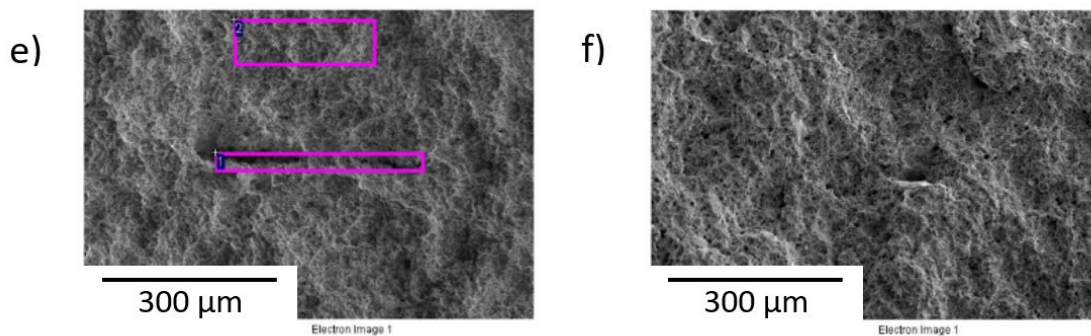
Superficie di frattura del provino in CW511L a cuore e) prima e f) dopo ricottura a 530°C per 2h (Raff. 40°C/h) / Fracture surface of the CW511L specimen in the core e) before and f) after annealing at 530°C for 2h (Cooling Rate 40°C/h).
